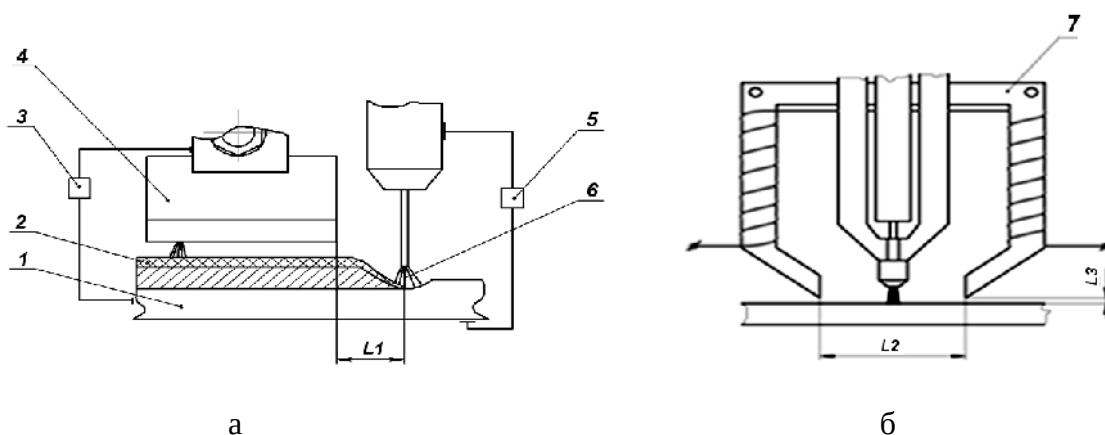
Конструкція пристрою для переміщення дуги (а) і схема розташування електромагніту (б): 1-основний метал (пластина для наплавлення); 2-наплавлений валик; 3-джерело живлення допоміжної дуги; 4-неплавка вугільна пластина; 5- джерело живлення основної дуги; 6-основна дуга; 7-електромагніт постійного струму
